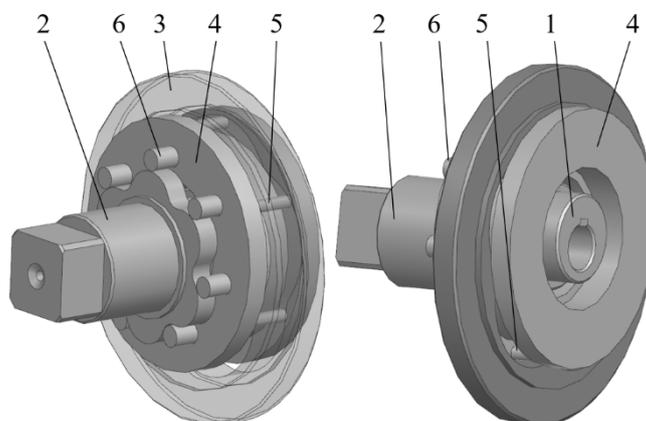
Циклоидально-цевочная передача: 1 – ведущий вал; 2 – ведомый вал с центральным циклоидальным колесом; 3 – корпус с центральным циклоидальным колесом; 4 – сателлит; 5, 6 – два венца сателлита с роликами
